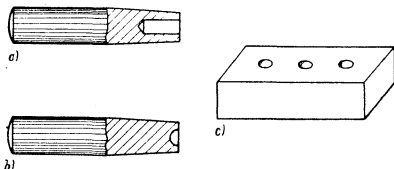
Nietwerkzeuge; Nietzieher (a), Nietkopfssetzer (b) und Gegenhalter (c) zum Einspannen in den Schraubstock
